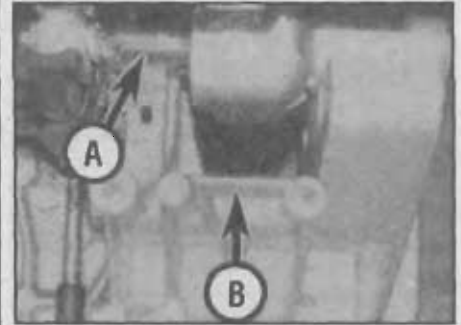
Установка вала рычага переключения передач (А) параллельно с ребром на отливке (В)
